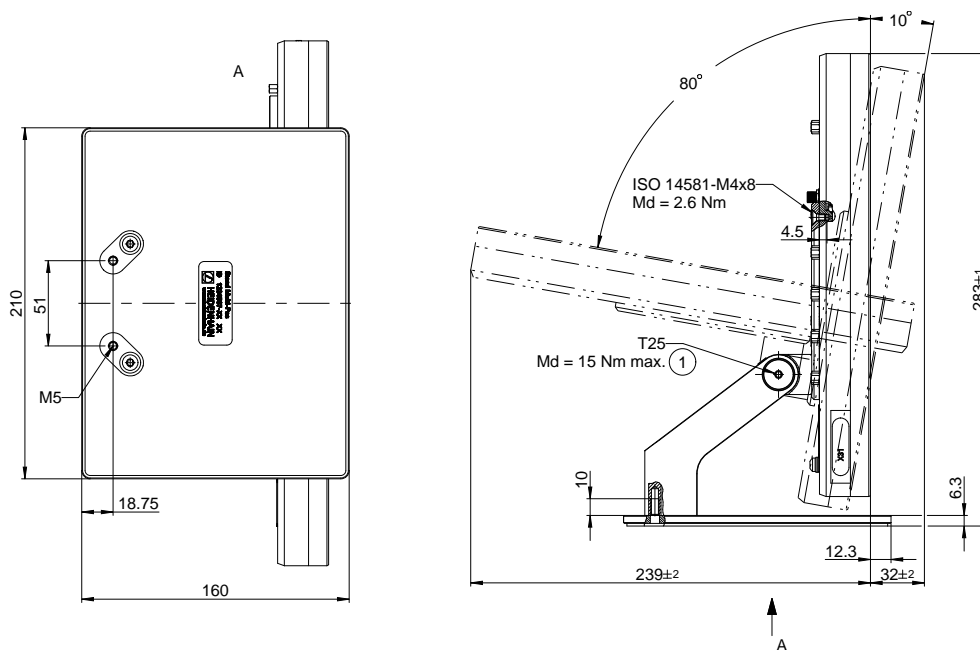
Dimensões do aparelho com pé de suporte Multi-Pos
